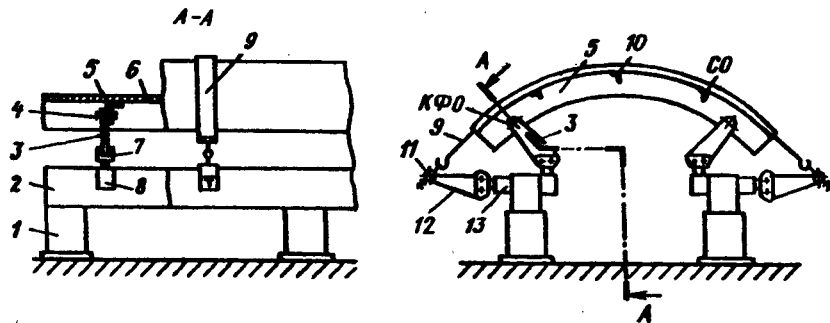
Сборно-разборное приспособление для сборки панелей
